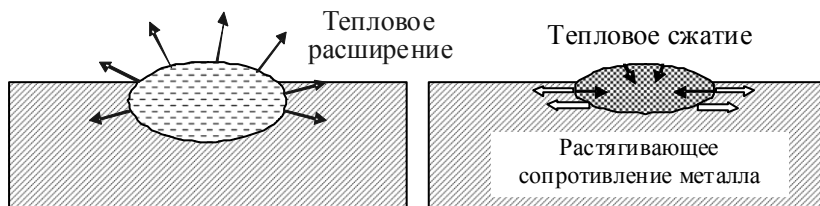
Образование напряжений при сварке. Расширение и плавление металла при нагреве, затвердевание и сжатие при остывании
